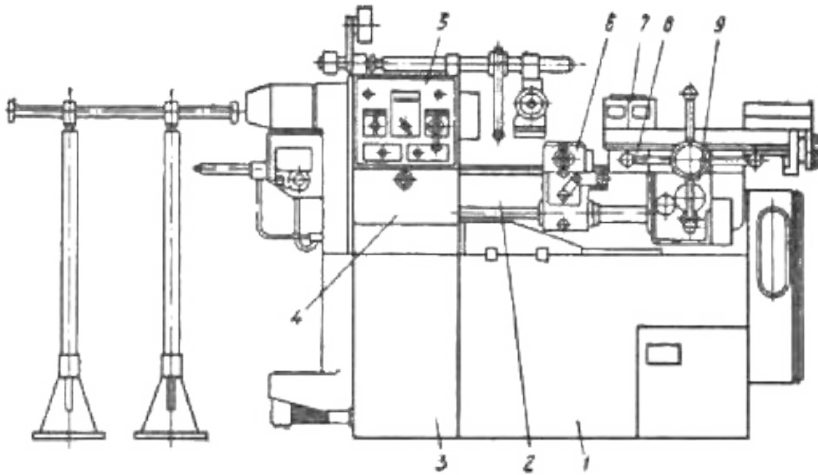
Токарно-револьверний верстат 1H325: 1 — корпус; 2 — станина; 3 — редуктор; 4 — коробка подач; 5 — шпіндельна бабка; 6 — поперечний супорт; 7 — шестипозиційна головка; 8 — каретка; 9 — фартух
